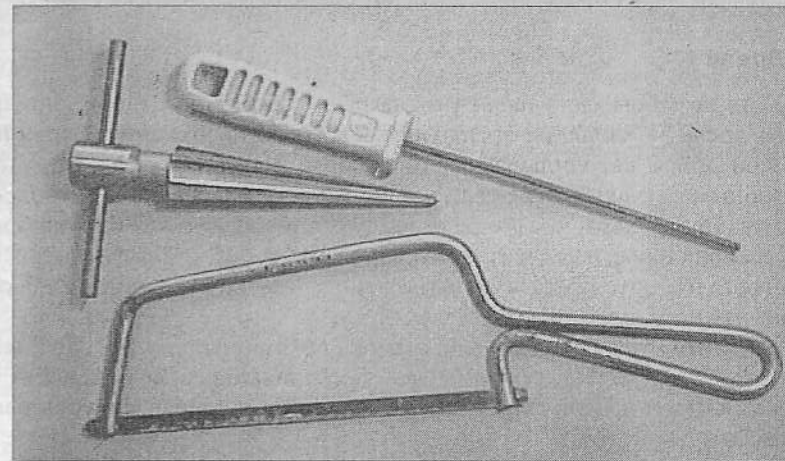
Круглый напильник, развертка и малая ножовка
